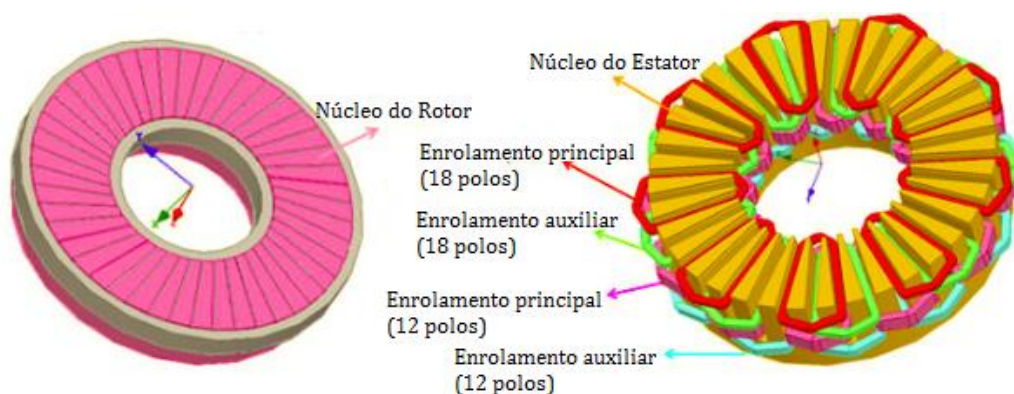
6. Configuração do gerador constituído por um estator de dupla face e um rotor duplo.
